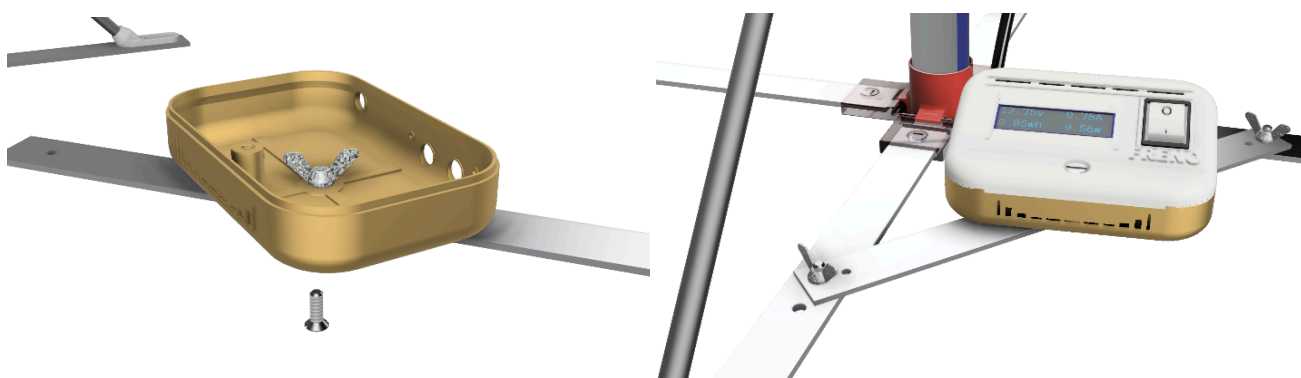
Consola fijada a la base articulada sobre la planchuela.
